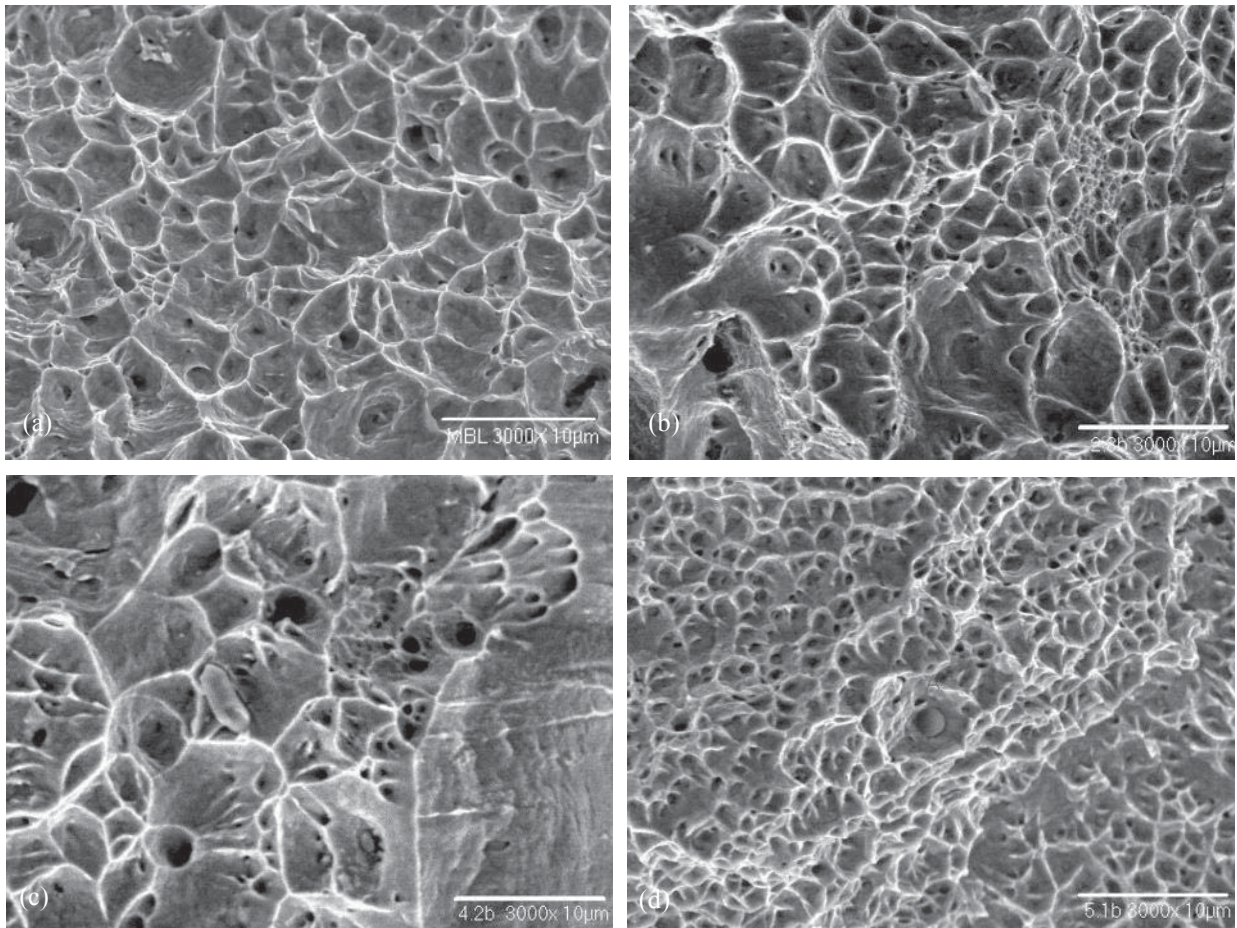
Fractografías del ensayo de tensión con unión en simple V 3000x (a) Material base (b) ZAT, soldada sin campo magnético (c) ZAT, soldada con campo magnético (d) ZAT, soldada con campo magnético y variando la orientación de las líneas flujo magnético.
